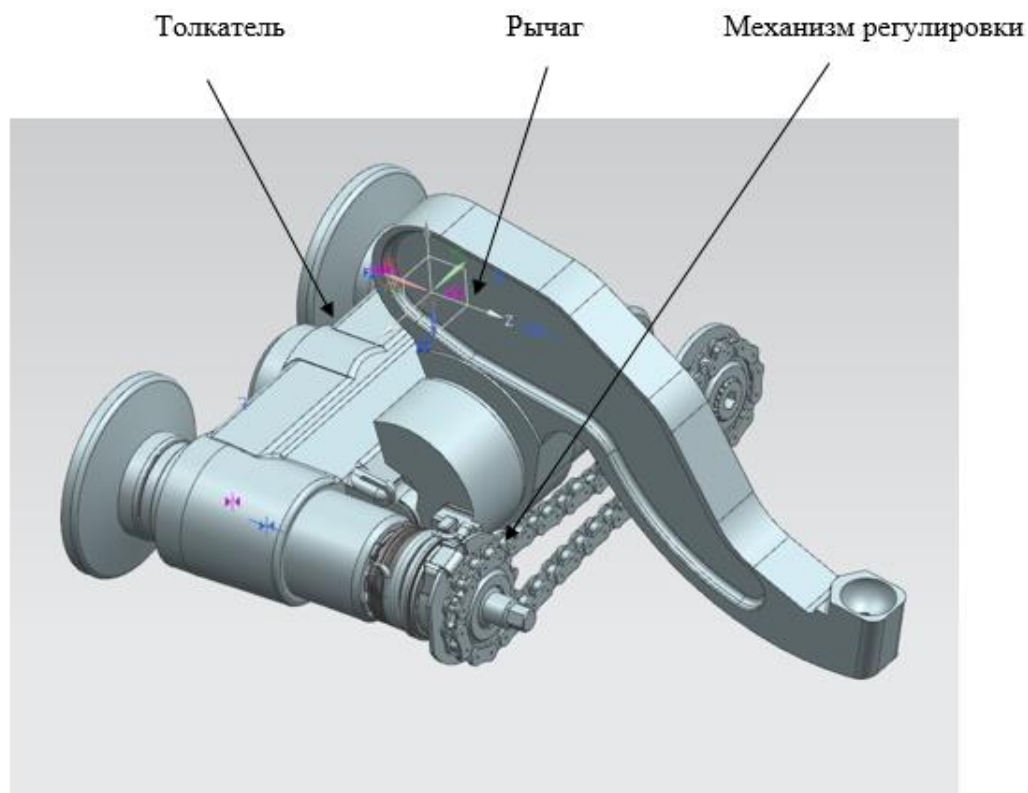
Установки механизма регулировки зазора в направляющей
